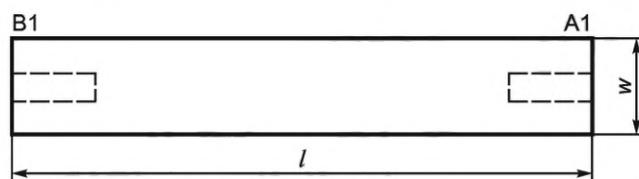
Образец, вырезаемый с короткой стороны планки
